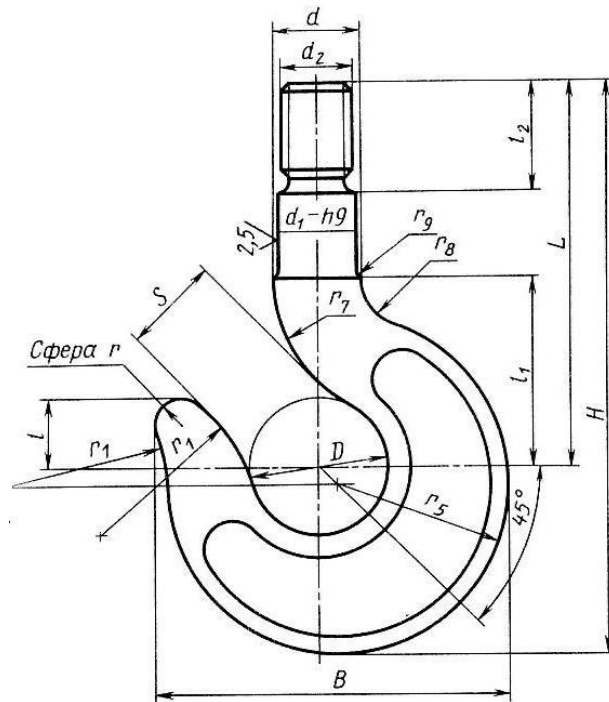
Заготовка кованого однорогого гака №17 тип Б.
